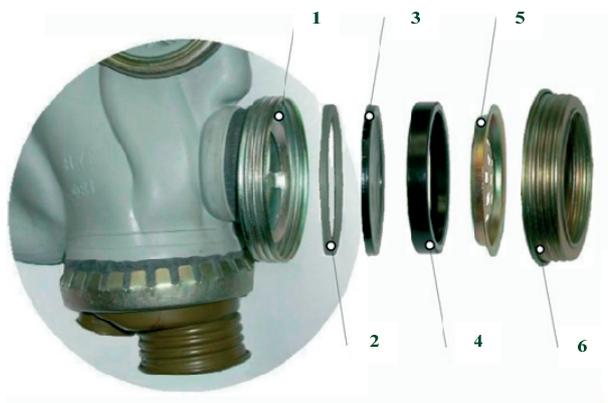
Переговорное устройство шлем-маски ШМ-66Му: 1 – корпус; 2 – резиновое кольцо; 3 – мембрана; 4 – опорное кольцо; 5 – крышка; 6 – фланец (у ШМГ – нажимное кольцо с решеткой)
